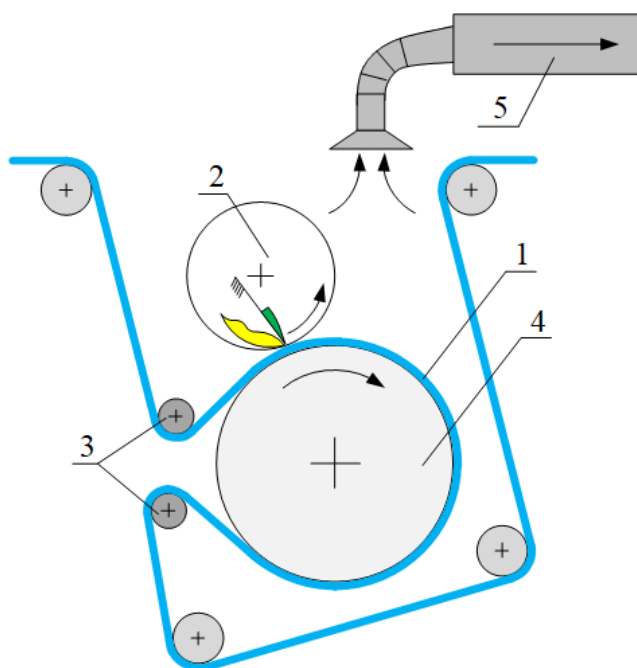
Схема узла машины для ТРП с валами, прижимающими пленку к поверхности печатного цилиндра: 1 – термоусадочная оболочка (пленка);
